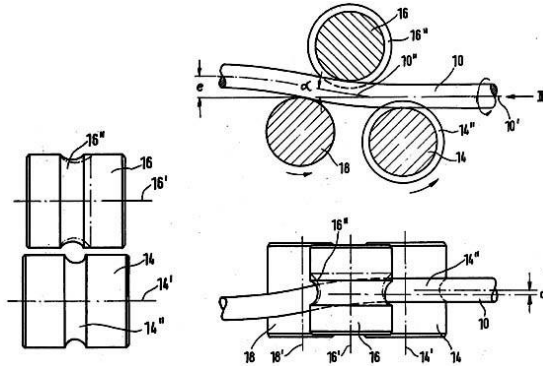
Rodillos laminadores utilizados por la máquina laminadora de rotores patentada por “Netsch-Mohnpumpen GMBH” (Frantisek, 1985).
